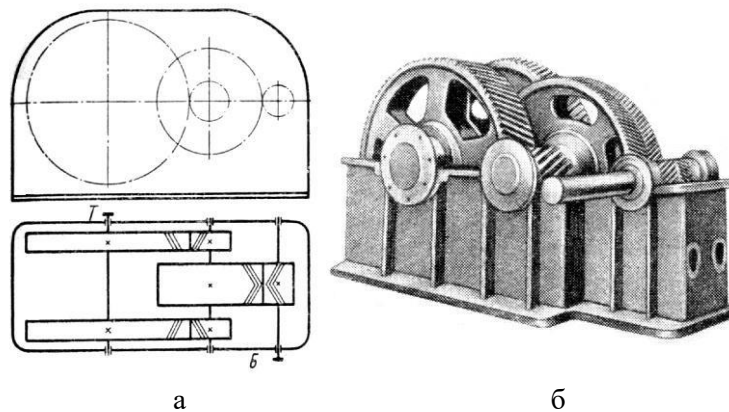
Двохступеневий горизонтальний редуктор з роздвоєною другою (тихохідної) щаблем Швидкохідний вал редуктора, показаного на рис. 7, б, повинен мати свободу осьового переміщення («плаваючий» вал), що забезпечується відповідною конструкцією підшипникових вузлів; в редукторі, показаному на рис. 8, а, свободу осьового переміщення, крім того, повинен мати тихохідний вал. При дотриманні зазначеного умови передана потужність розподіляється порівну між паралельно працюючими парами зубчастих коліс. В результаті в небезпечному поперечному перерізі проміжного вала виникає
